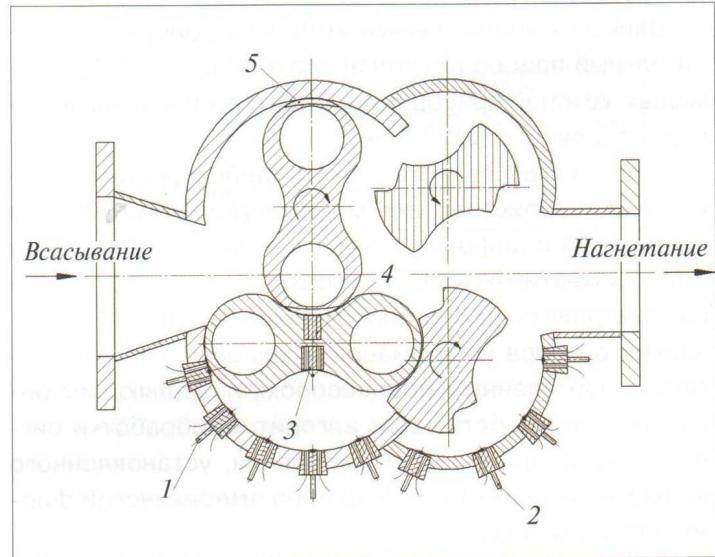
Расположение датчиков на корпусе и роторе компрессора:
